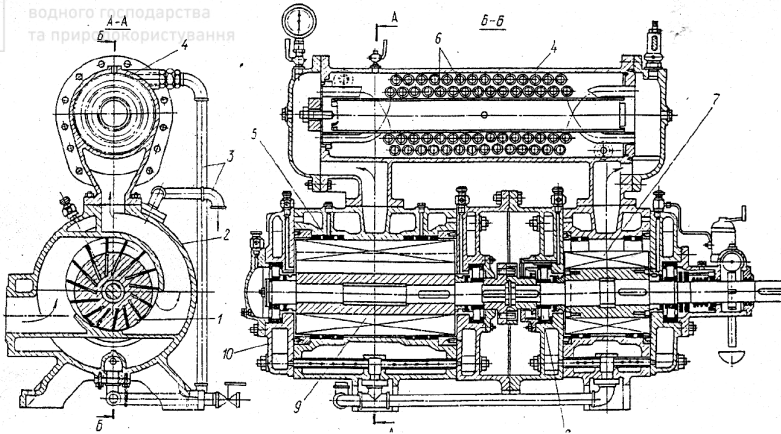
Пластинчастий двохступінчастий компресор: 1- ротор, 2- корпус; 3- труби для підводу і відводу охолоджуючої води; 4- охолоджувач; 5- розвантажувальні кільця; 6- охолоджуючі труби; 7- пластина (шибер) другого ступеня; 10-кришка
